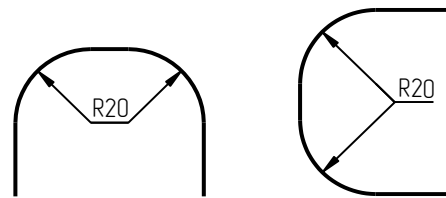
Одинаковые скругления допускается указывать на *общей* полке размерных линий, располагая размерные числа удобным для чтения образом
